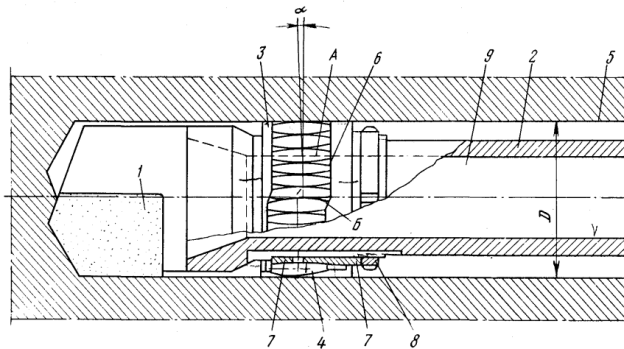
Свердло для глибокого свердління із самоподачею
